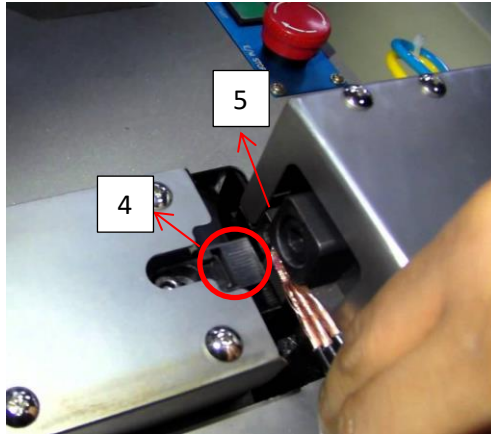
Componentes da zona de soldadura: (4) garra deslizante; (5) placa de superfície com encaixe [15]
